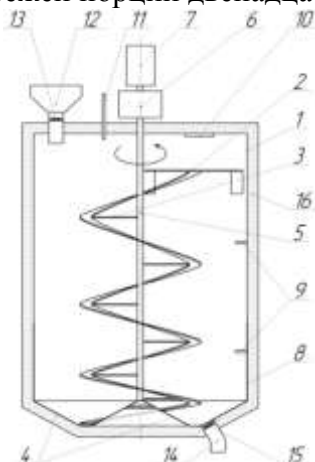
Конструктивная схема биогазовой установки. 1 – корпус, 2 – ленточная мешалка с гребнем, 3 – лучи к которым
